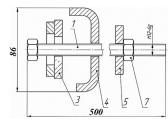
Болт из набора «СНКЛ-3 ССД» с крепёжными деталями: 1 – болт; 3 – накладка; 4 – швеллер; 5 – шайба; 7 – гайка М12.
